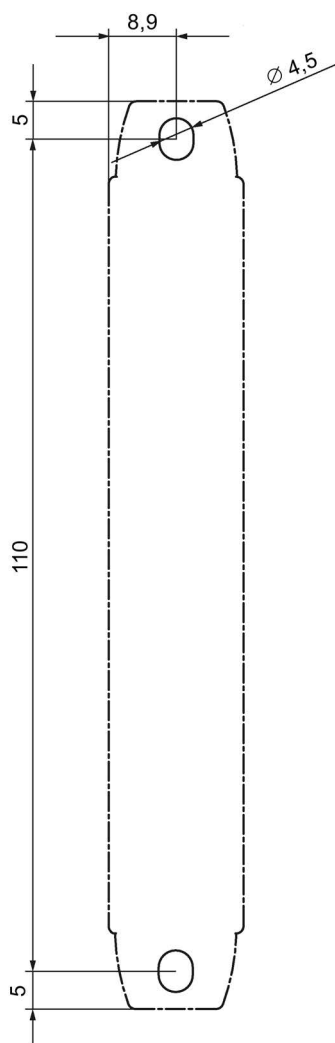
Bohrplan Gehäuse 17,5 mm
